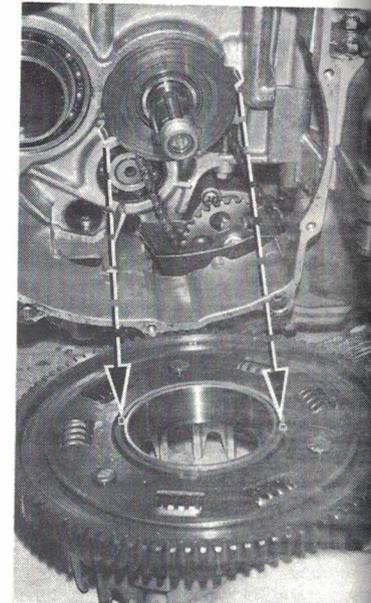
Entraînement de la cloche à huile (Photo RMT)
